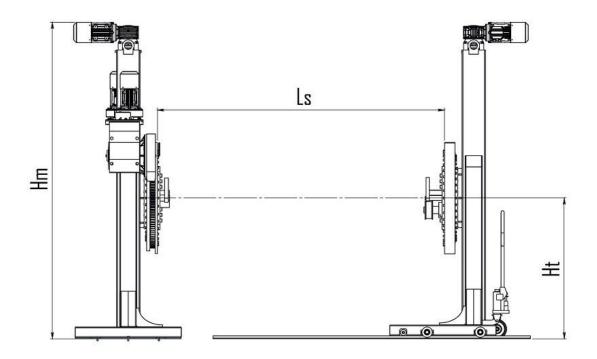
Двухстоечный сварочный вращатель серии *BEM*.
